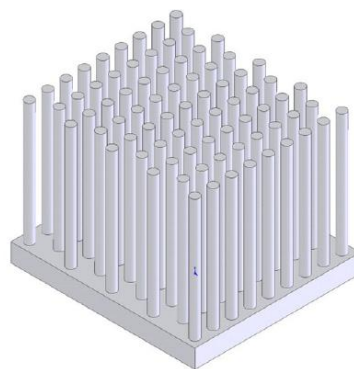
Vue en perspective de la géométrie du dissipateur de chaleur [54].
